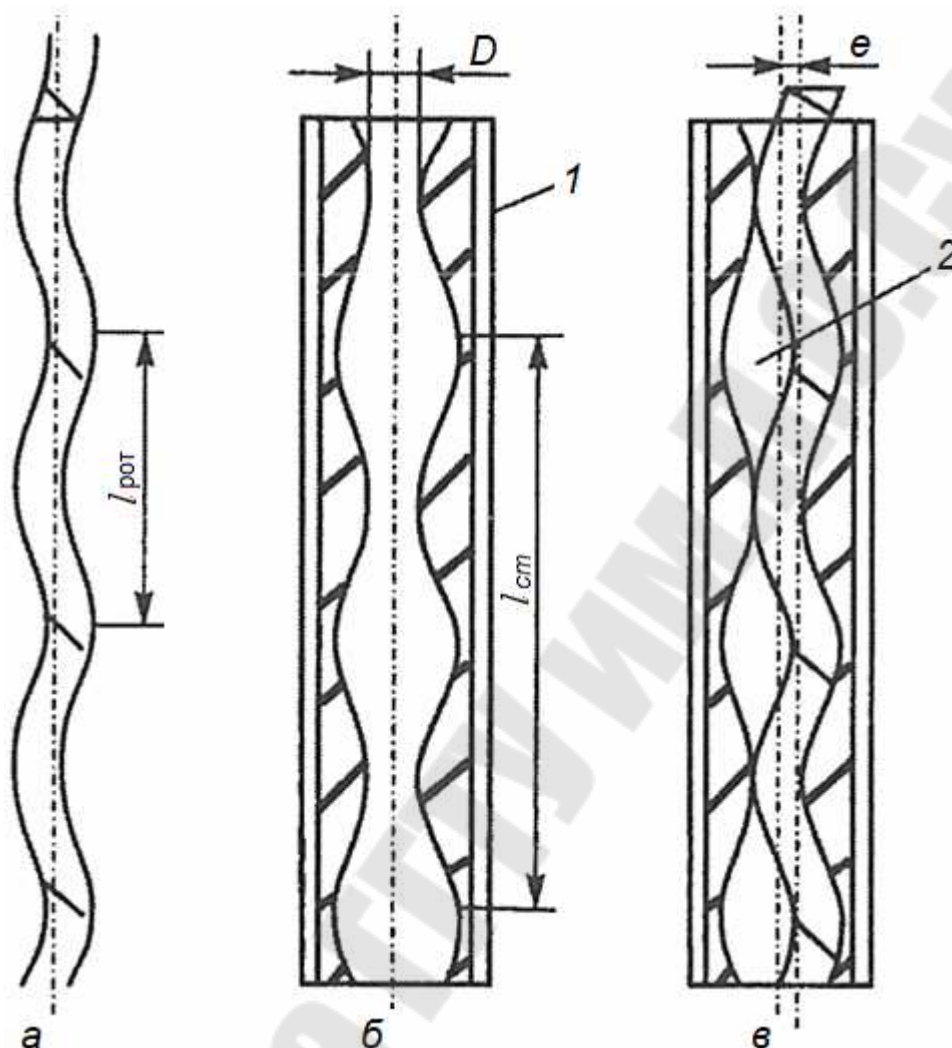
Принципиальная схема устройства винтового насоса: а – ротор; б – статор; в – насос в сборе; 1 – корпус насоса; 2 – полость между ротором и статором
